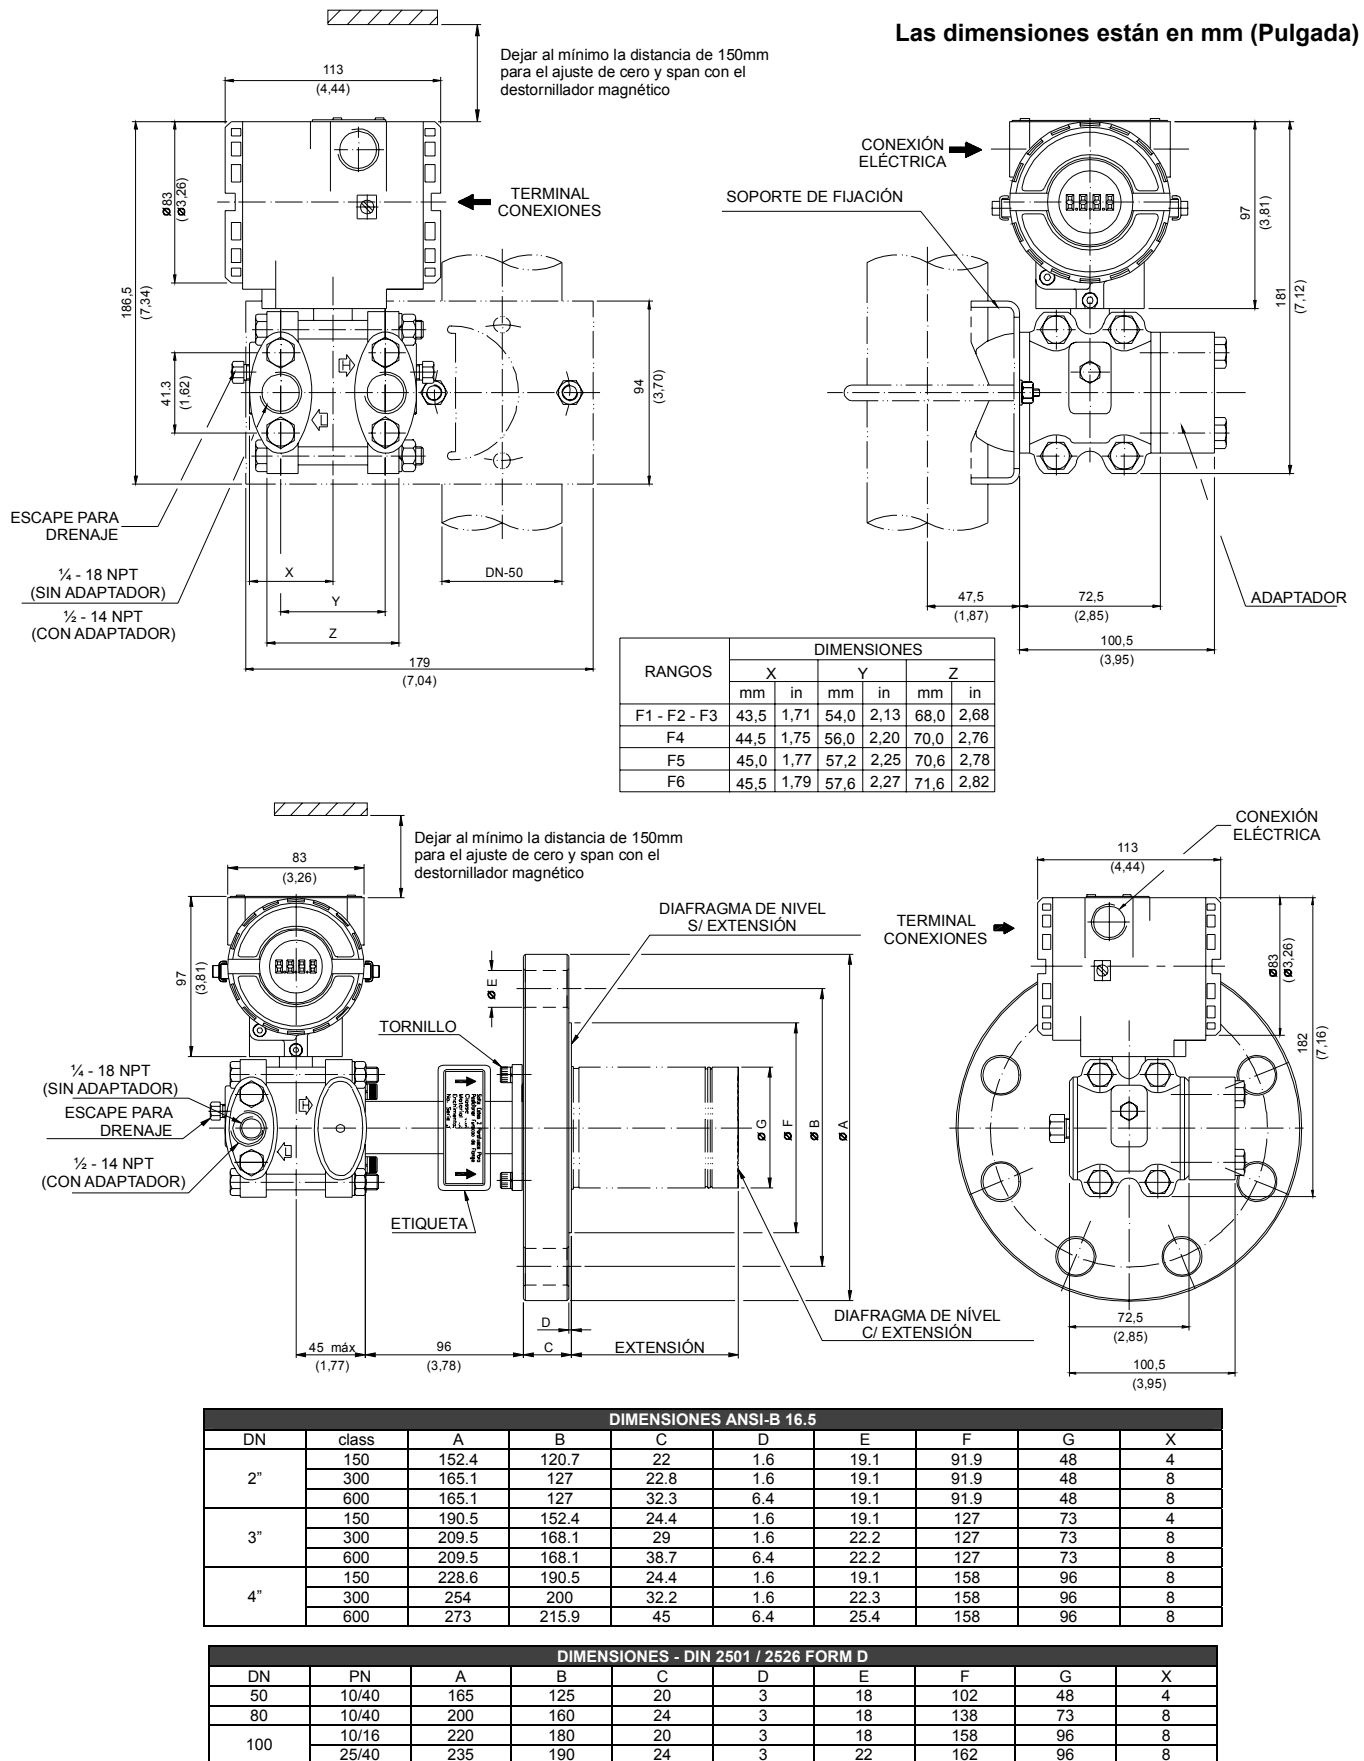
Diseño Dimencional de Montaje del LD301
